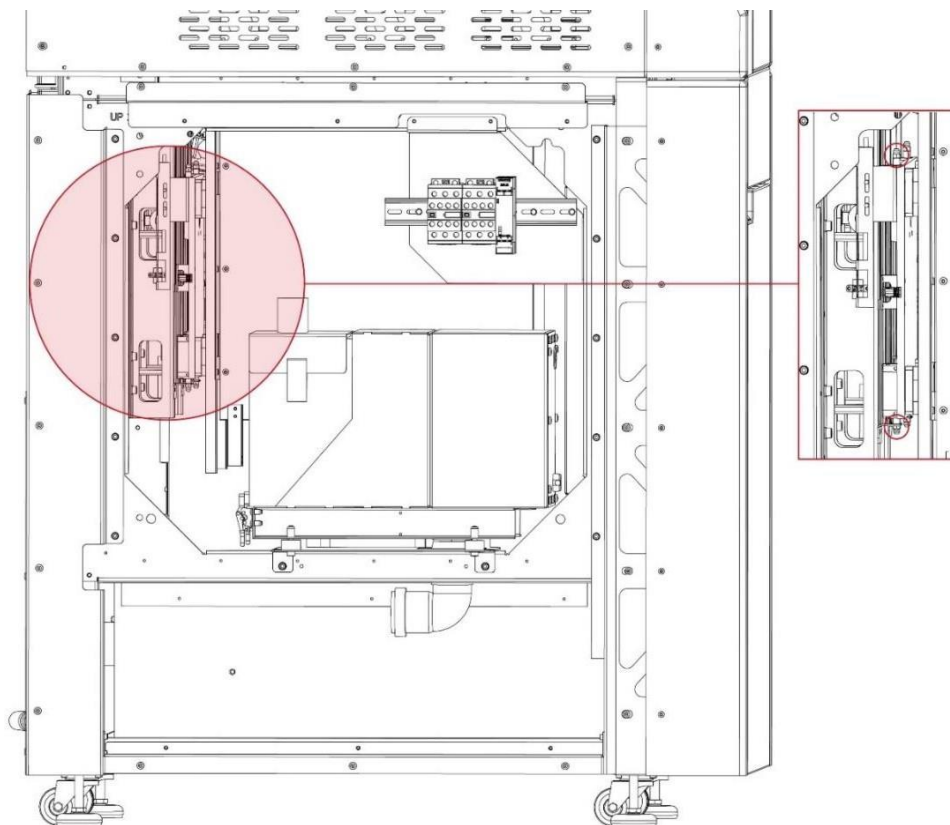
Месторасположение смазочных ниппелей - вид сбоку.
